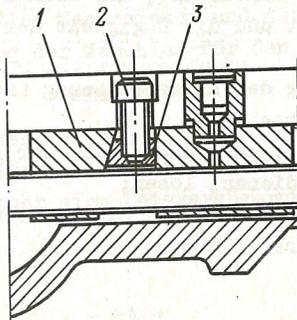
Einstellung des Spiels in der Schloßmutter des Planschlittens
